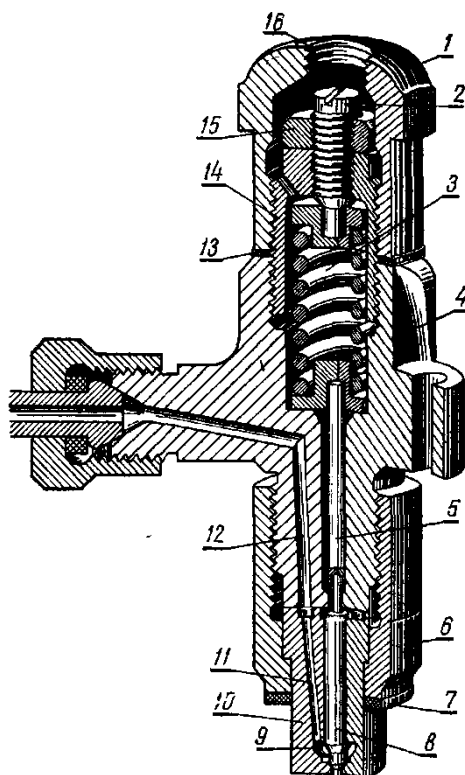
Форсунка ФШ-1,5Х25°:
